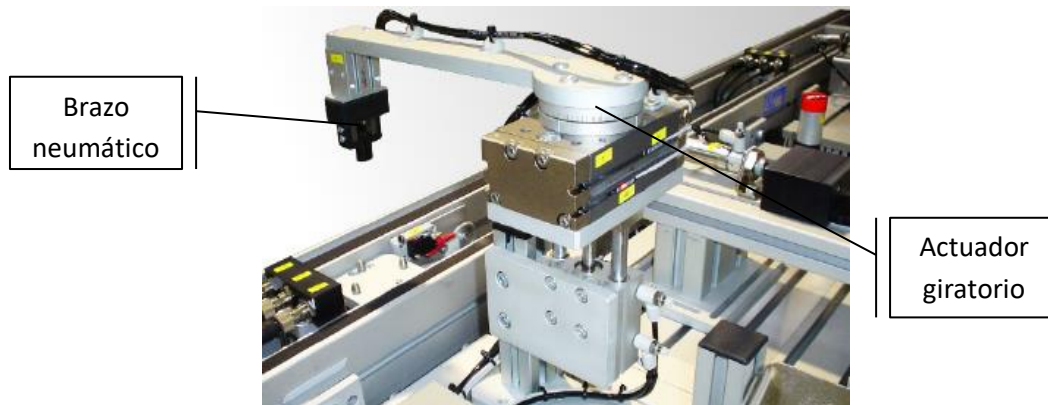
Inserción del rodamiento en la base. Fuente: (www.smc.eu).
